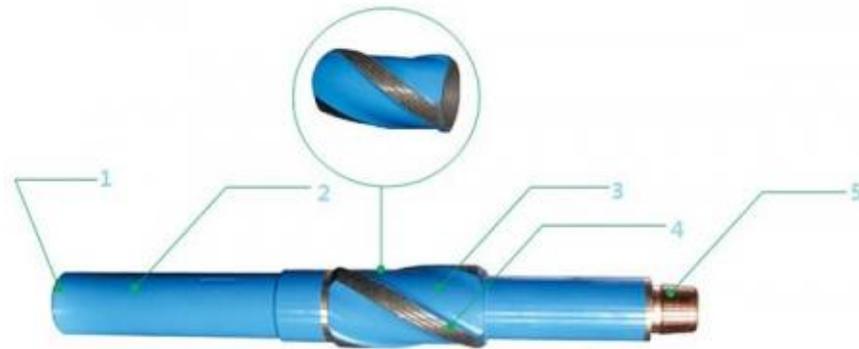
Стабилизатор с несъемными фрезерованными лопастями
